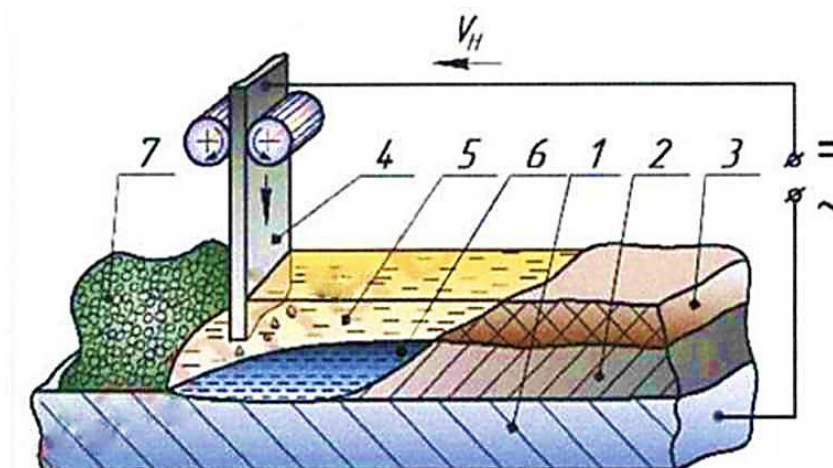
Схема процесу електрошлакового наплавлення: 1 - основний метал; 2 - наплавлений метал; 3 - шлакова кірка; 4 - смуга наплавленого металу; 5 - шлакова ванна; 6 - кристалізатор; 7 - зварювальний флюс.
